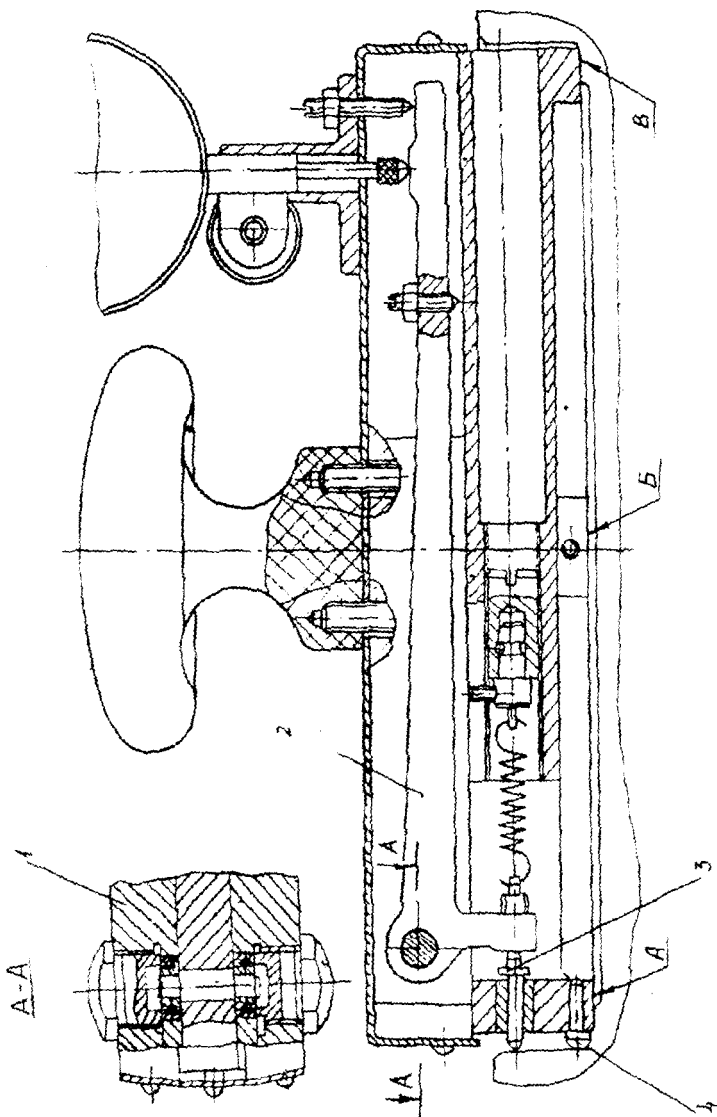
Приспособление для контроля перпендикулярности обрабатываемой наружной поверхности относительно торца детали
